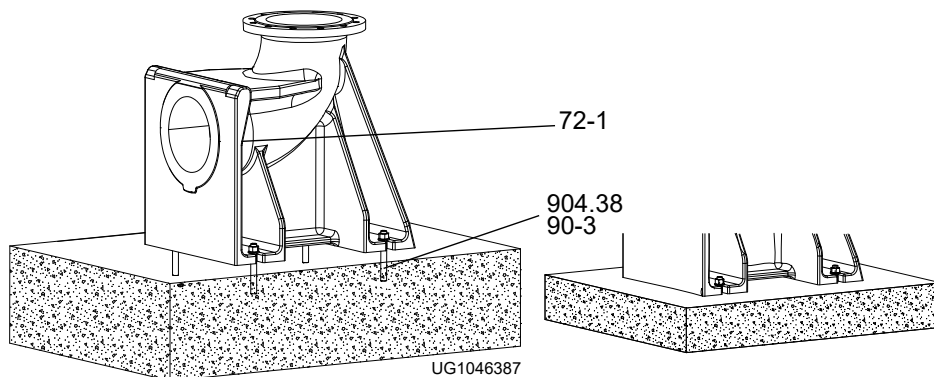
Flanschkrümmer mit Verbundankern befestigen
